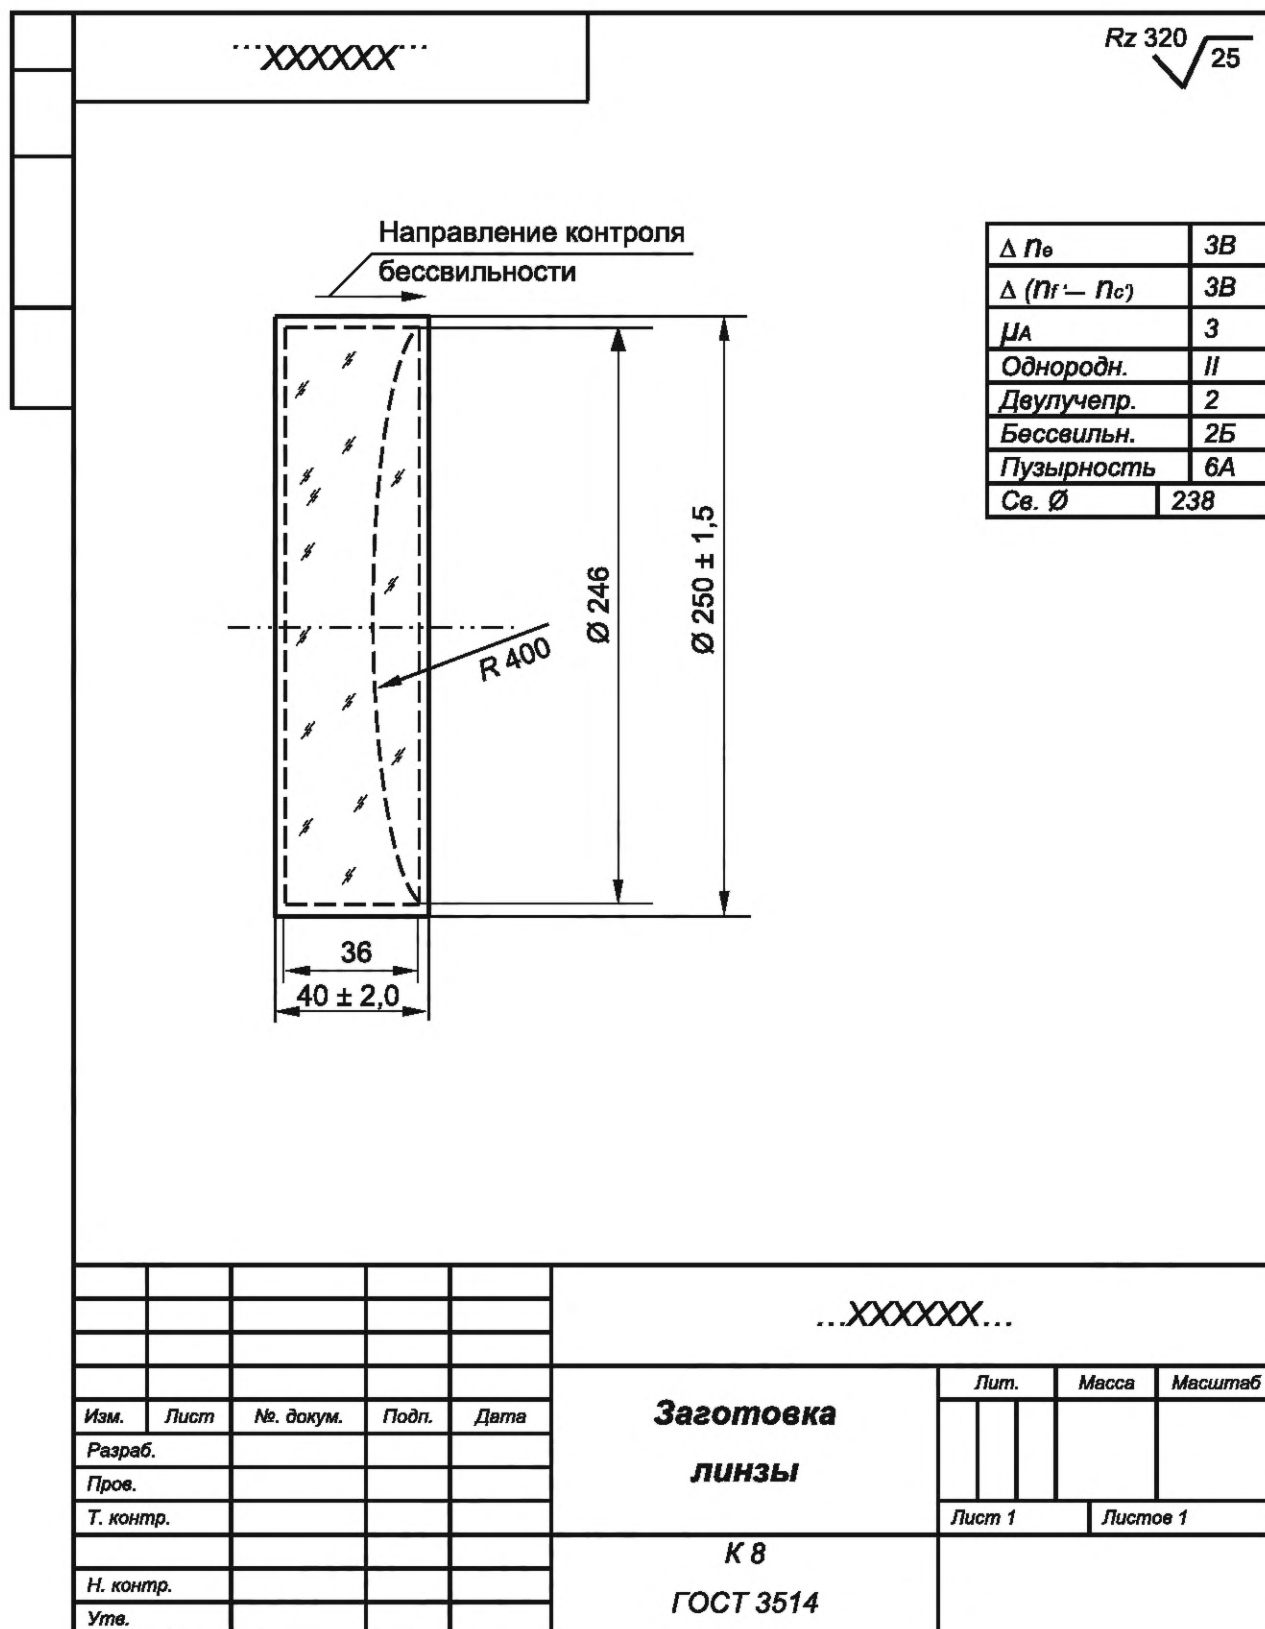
Чертеж заготовки линзы из стекла марки К 8 по ГОСТ 3514
